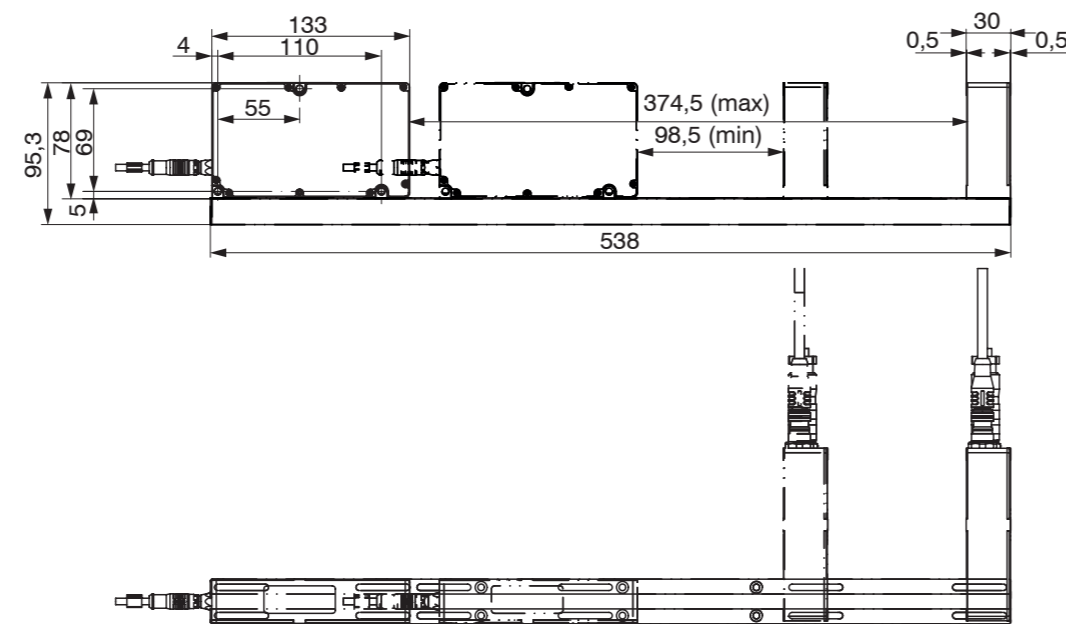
Maßzeichnung ODC 2520-46(090) Lichtquelle und Empfänger mit Montageschiene, Abmessungen in mm
